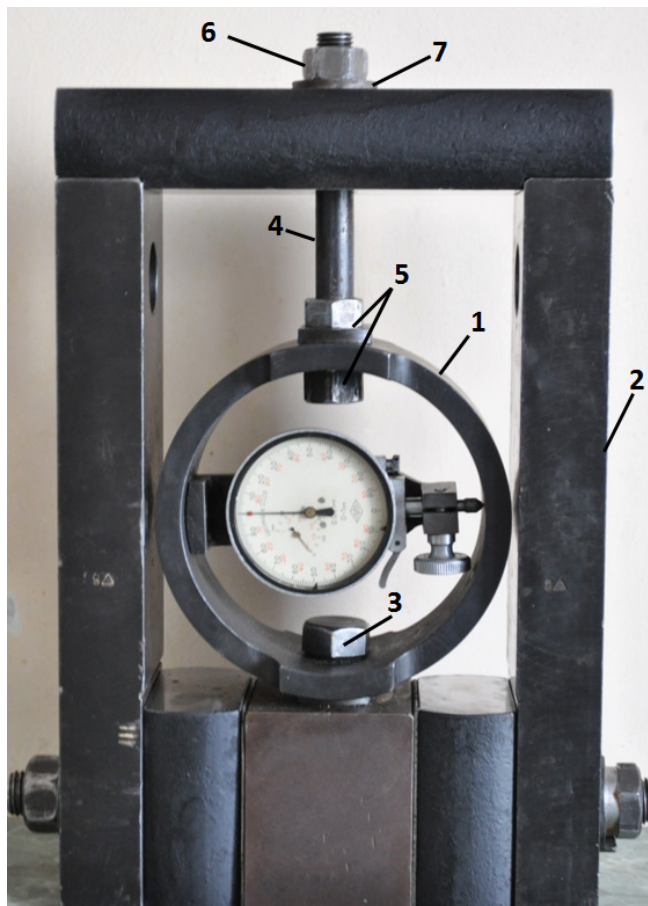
Приспособление для нагружения резьбовых пар «шпилька-гайка»
